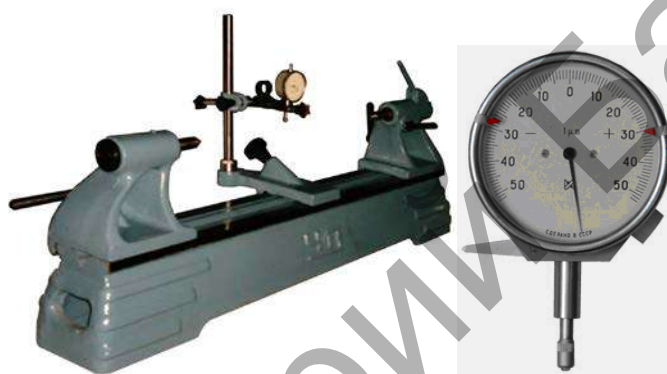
Прибор для проверки биения ПБ-250 и рычажно-зубчатая головка ИИГ
